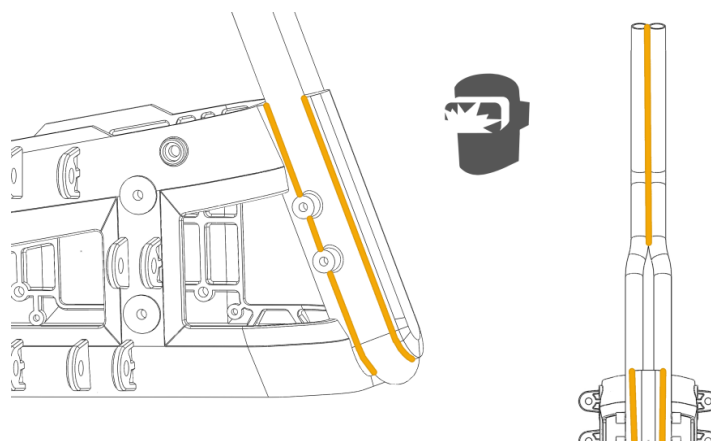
Zones on s'aplica cordó de soldadura
